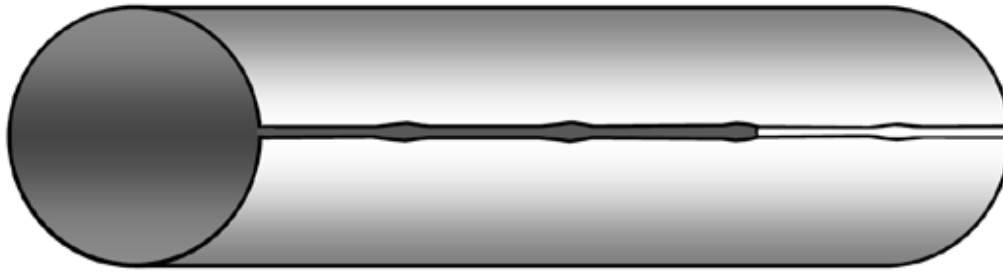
Вид неровной кромки с гофрами листовой заготовки после кромкогибочного и трубоформовочного прессов перед сваркой продольного шва трубы
